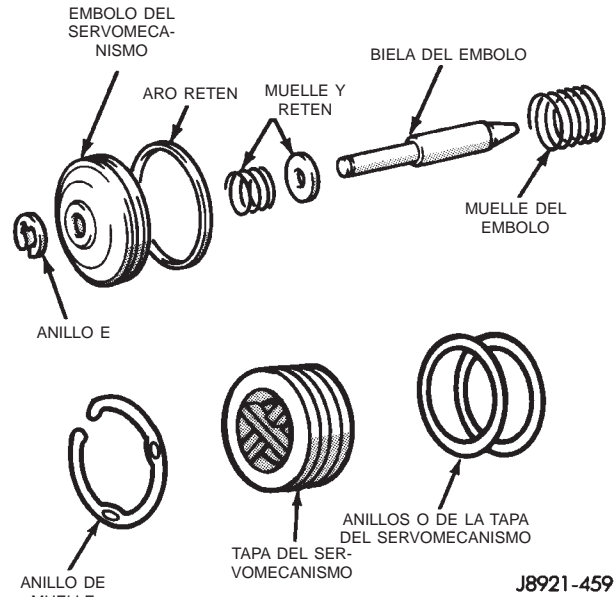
Componentes del servofreno de rodadura libre en segunda
